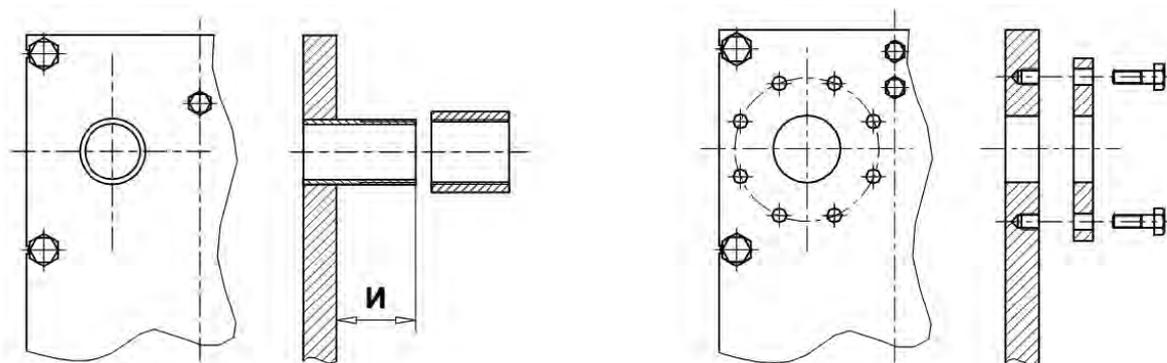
Схема установки теплообменника на фундаментную раму
